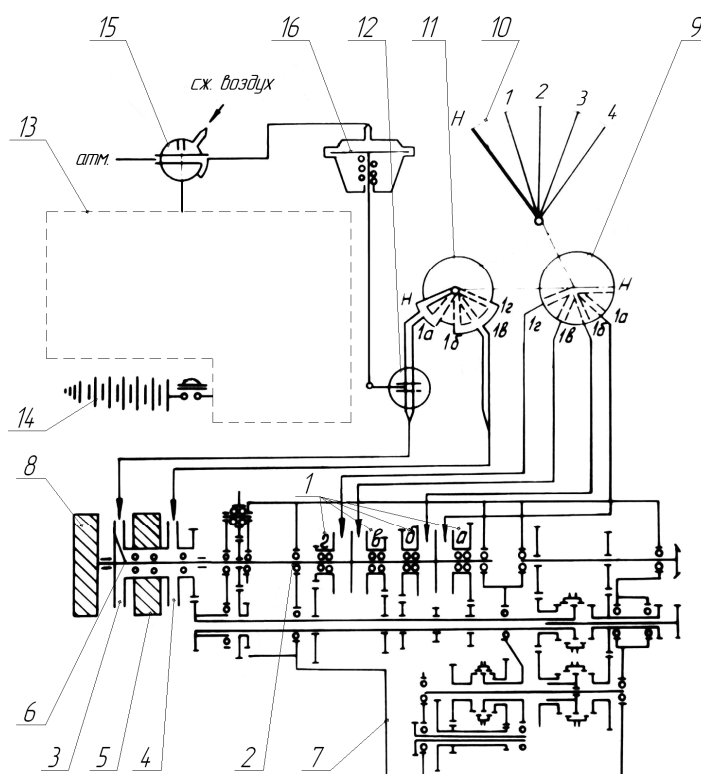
Установка для автоматического управления дополнительной вращающейся массой двигателя
